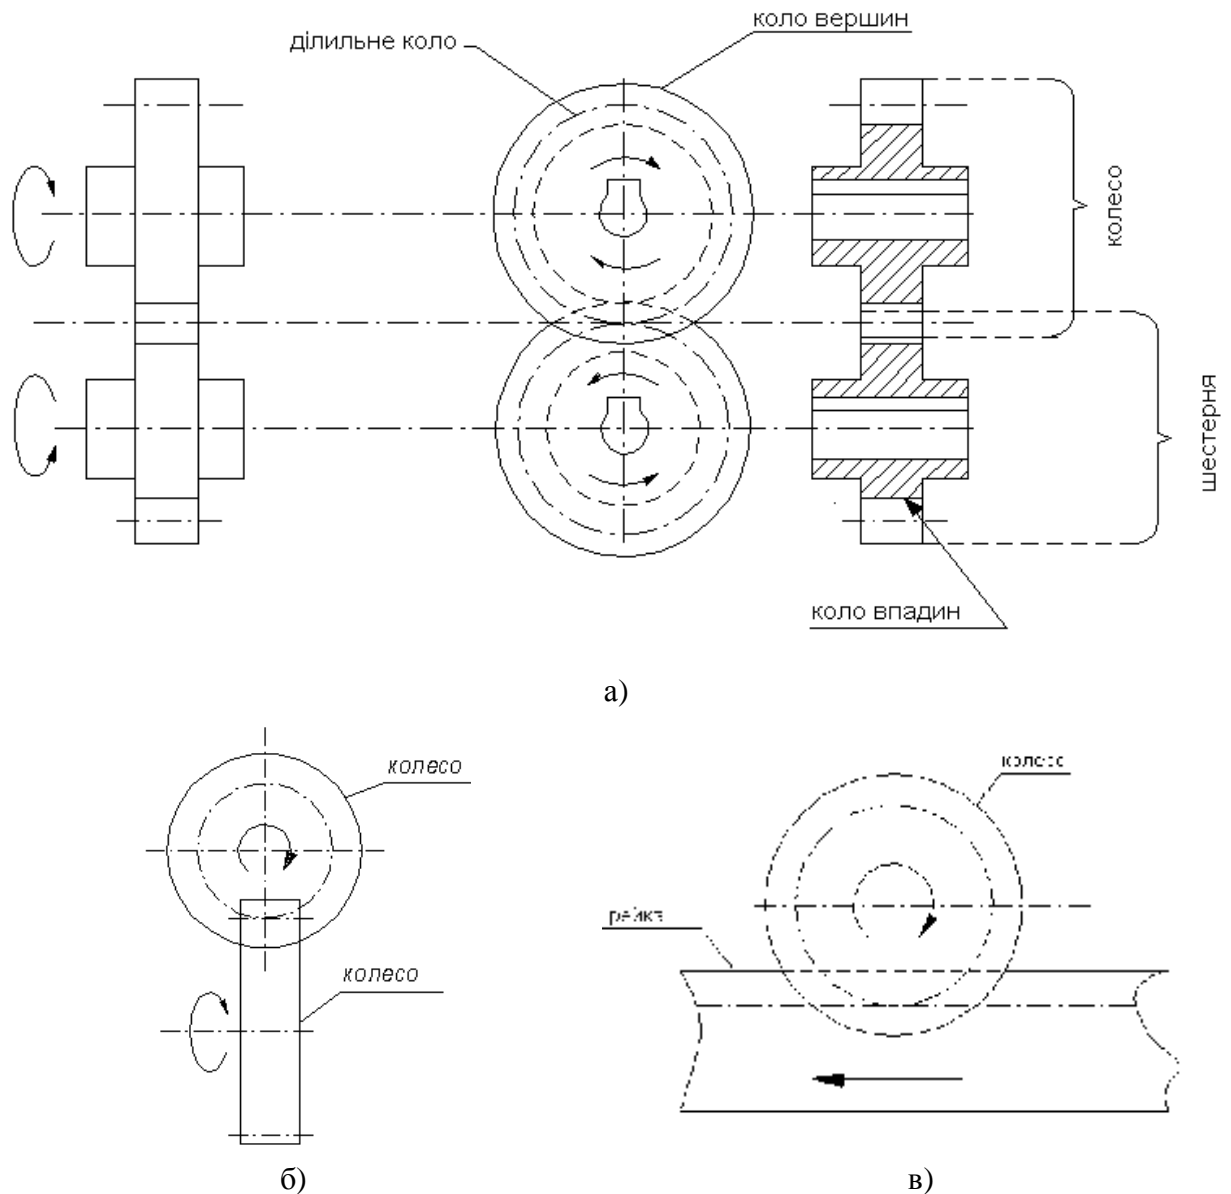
Приклади зображення зубчастих передач на кресленнях: а – циліндрична зубчаста передача з паралельними осями; б – циліндричні зубчасті передачі з перехресними осями; в – передача колесо-рейка
